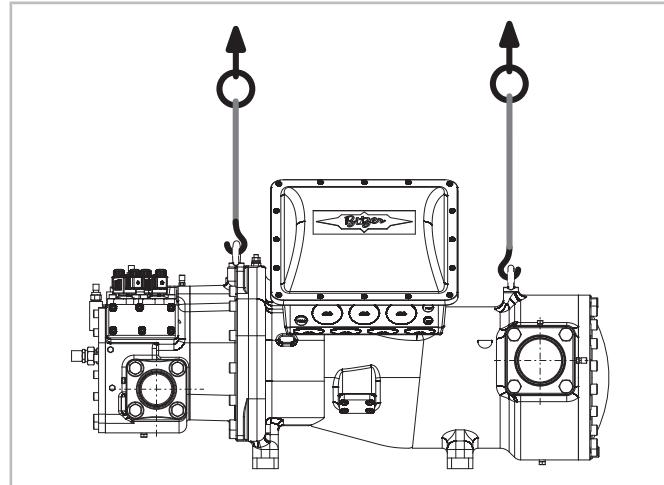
Standard: Soulever les compresseurs, suspension à deux points : Exemple HS.85
